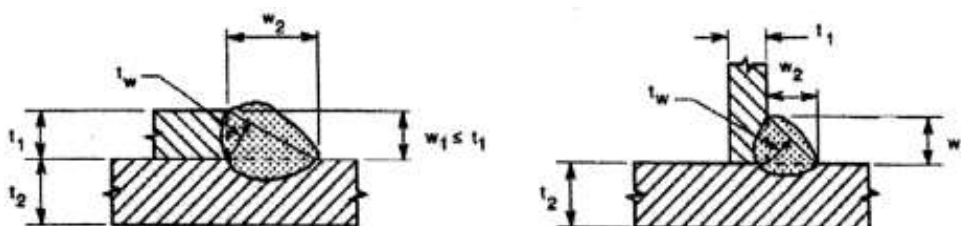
(a) Soldadura transversal; (b) Soldadura longitudinal
